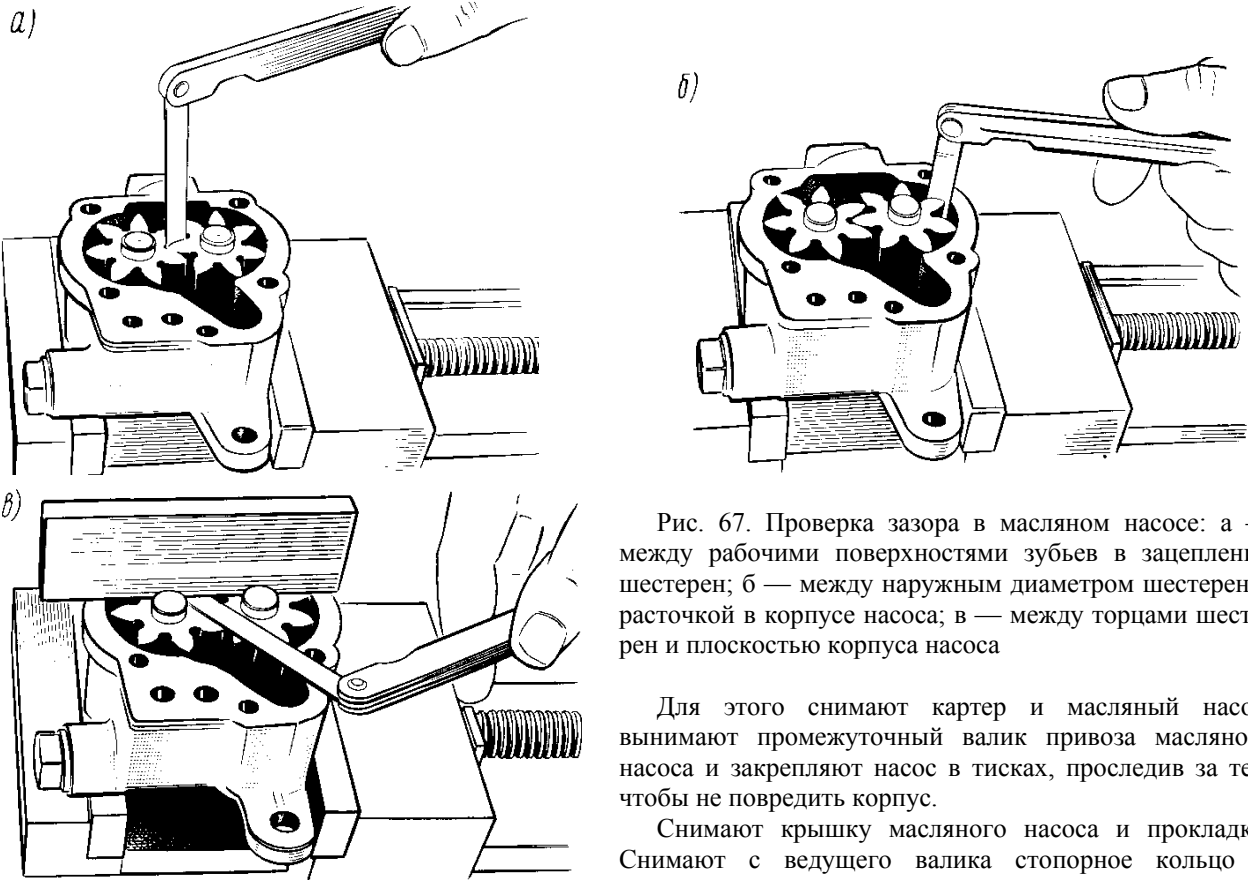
Проверка зазора в масляном насосе: а — между рабочими поверхностями зубьев в зацеплении шестерен; б — между наружным диаметром шестерен и расточкой в корпусе насоса; в — между торцами шестерен и плоскостью корпуса насоса
